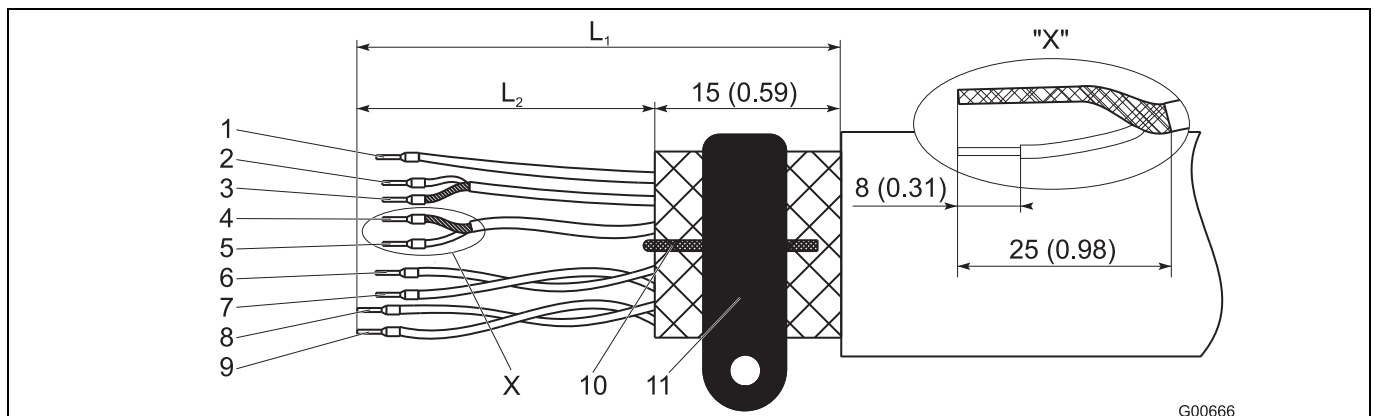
Côté transmetteur, dimensions en mm (inch)
